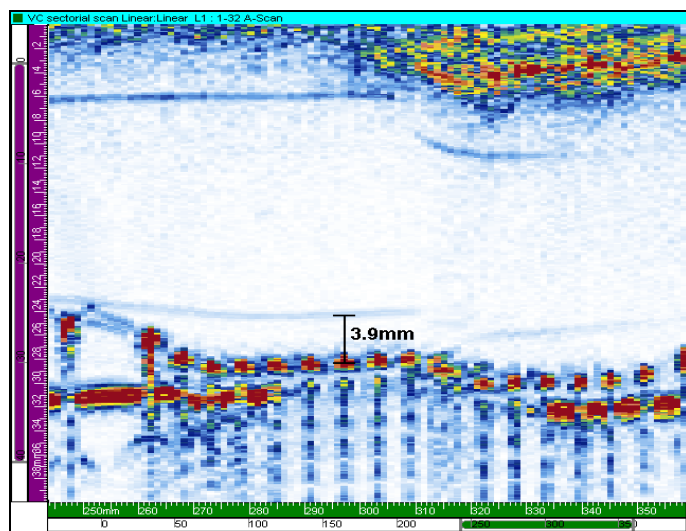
IMAGEN DE UNA UNIÓN POR EF EN UNA TUBERÍA DE PE DE 450 MM CON SOLDADURA FRÍA
